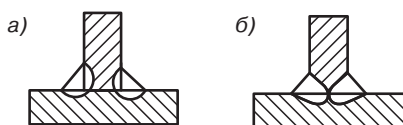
Тавровые соединения: а — угловыми швами без разделки кромок; б — стыковыми швами с разделкой кромок
